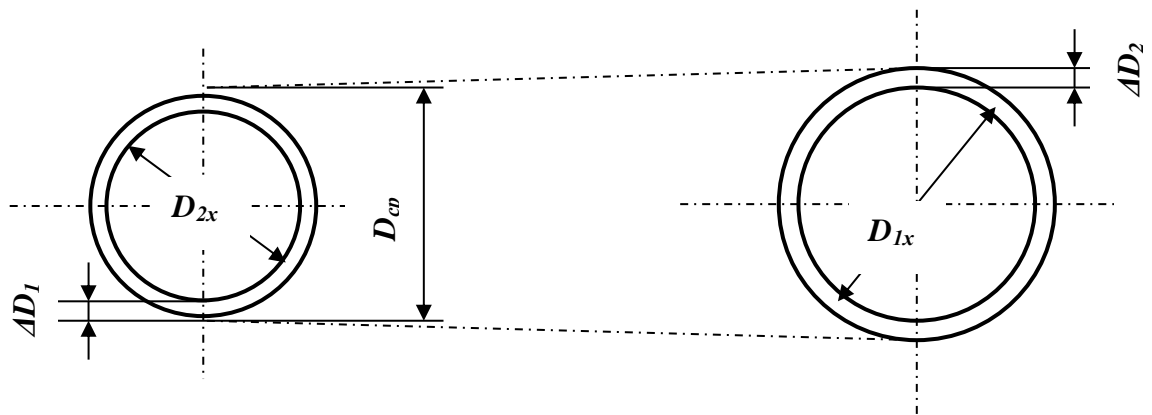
Розрахункова схема регулювання варіатора
